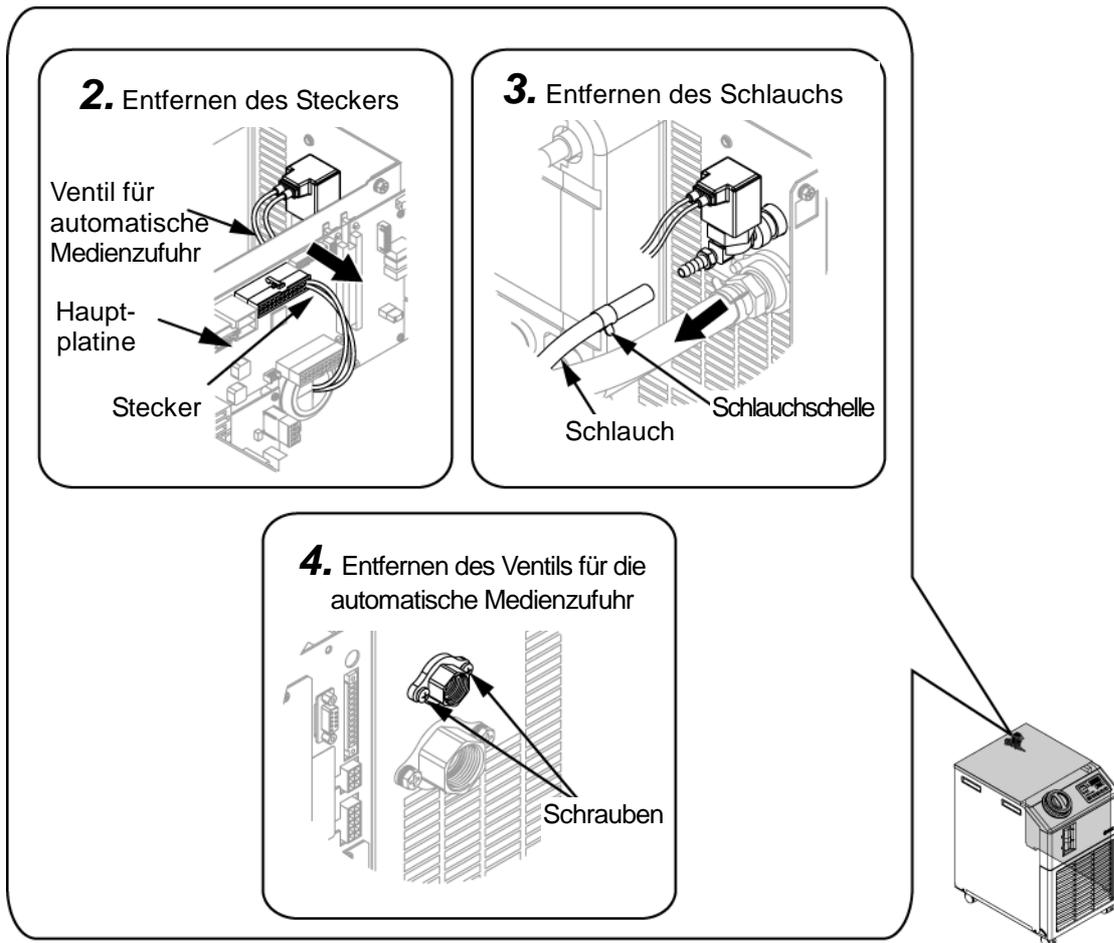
Entfernen des Ventils für die automatische Medienzufuhr
